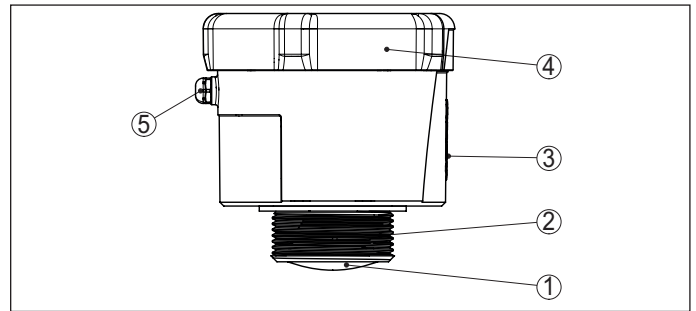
Komponenten des Radarsensors VEGAPULS Air 41 (Beispiel Ausführung mit Gewinde G1 1/2)
